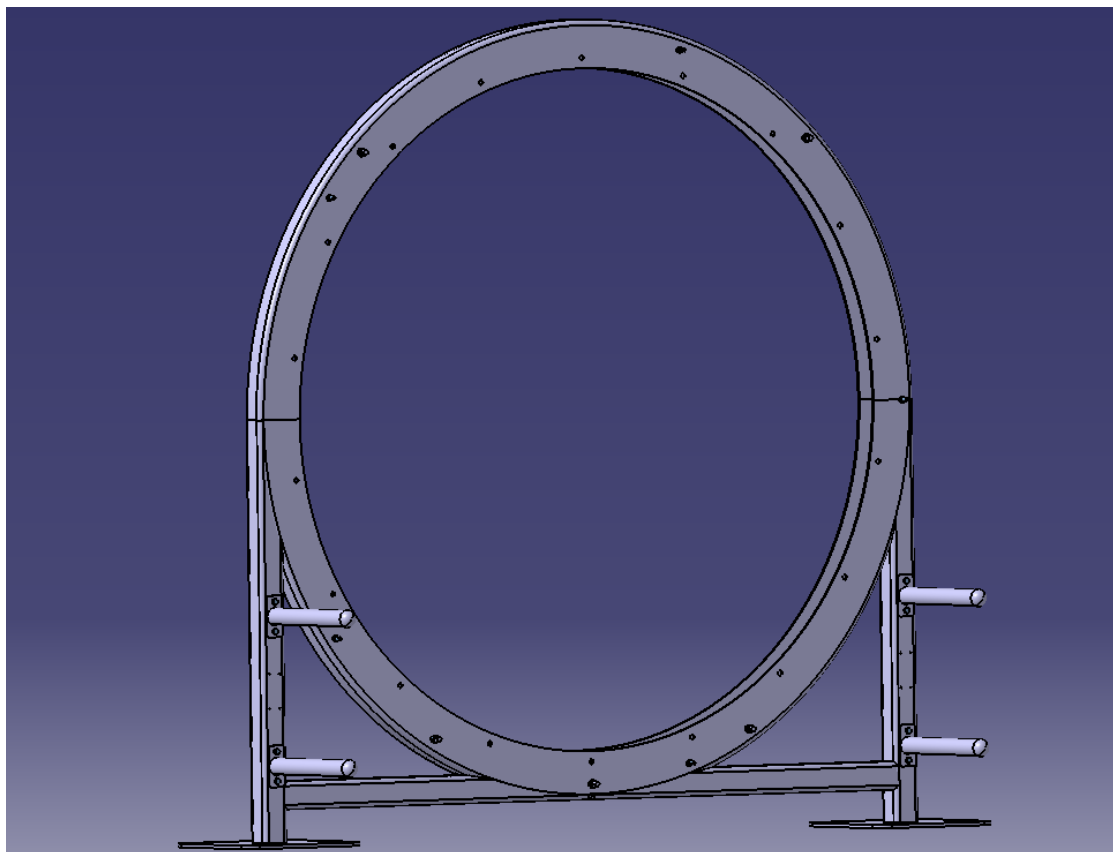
Cubierta, patas y soporte soldados.
